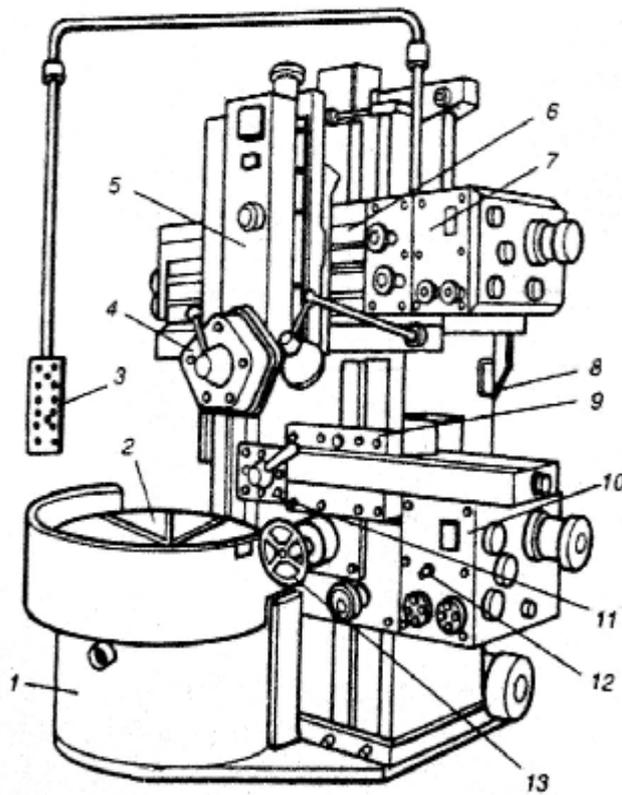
Токарно-карусельный станок одностоечный: 1 – станина; 2 – планшайба; 3 – пульт управления; 4 – револьверная пятипозиционная головка; 5 – суппорт; 6 – траверса; 7, 12 – коробки подач; 8, 13 – маховички; 9 – стойка; 10 – суппорт боковой; 11 – резцедержатель четырехпозиционный
